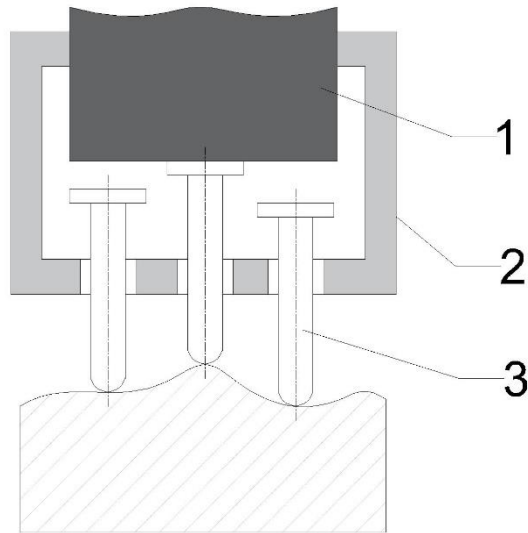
Схема рабочего узла многоэлементного инструмента для обработки сварных швов:
